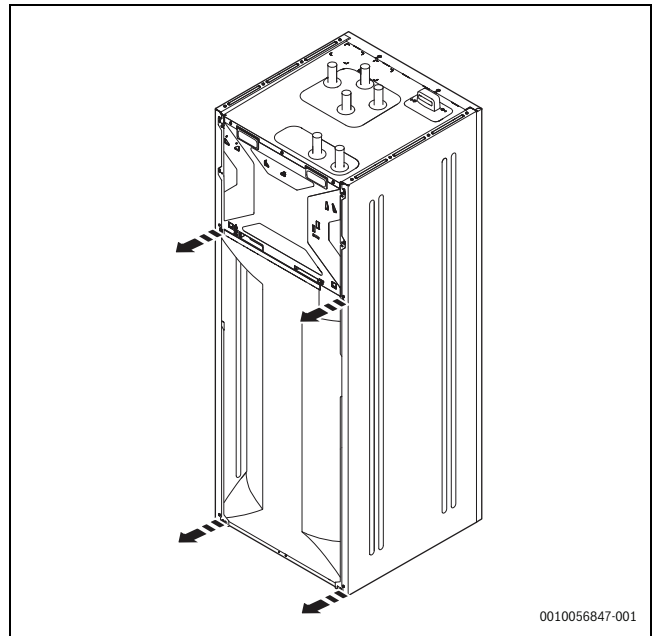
Schrauben für Demontage der Seitenwände entfernen
